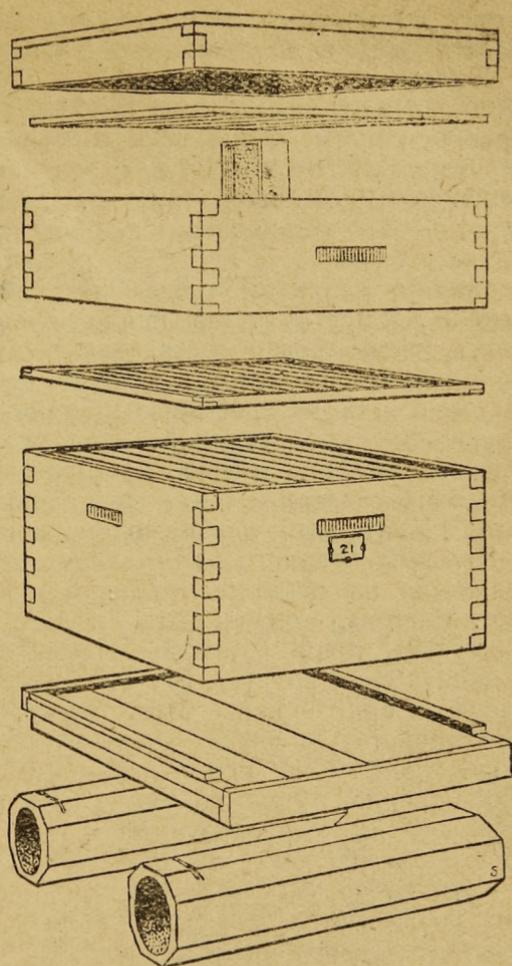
10-рамочный улей с надставкой для сотового меда и цинковый исключатель для маток.
